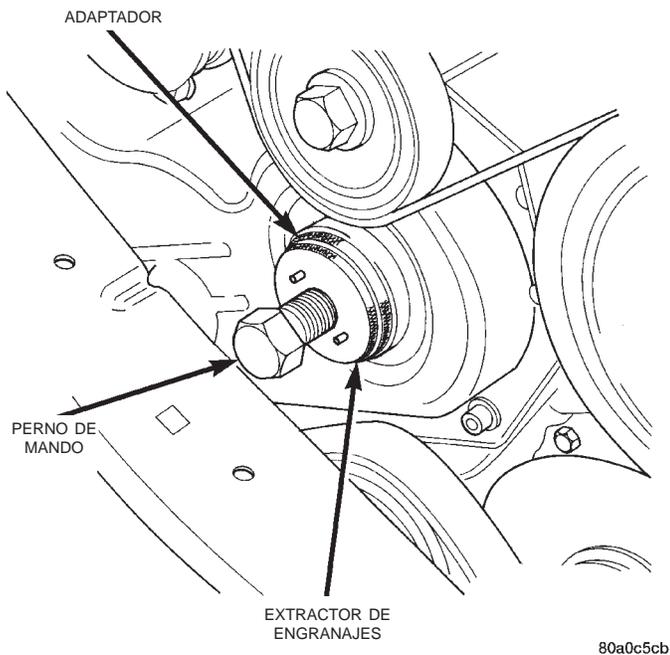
Instalación de las herramientas de desmontaje del engranaje propulsor de la bomba
